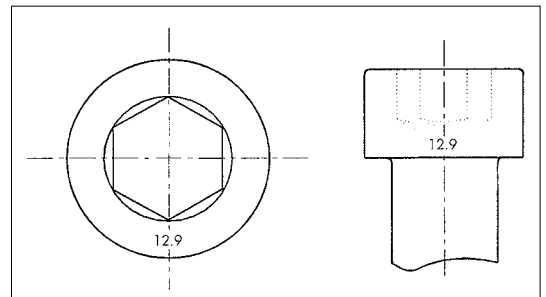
Abb. H: Beispiel für die Kennzeichnung von Zylinderschrauben mit Innensechskant
